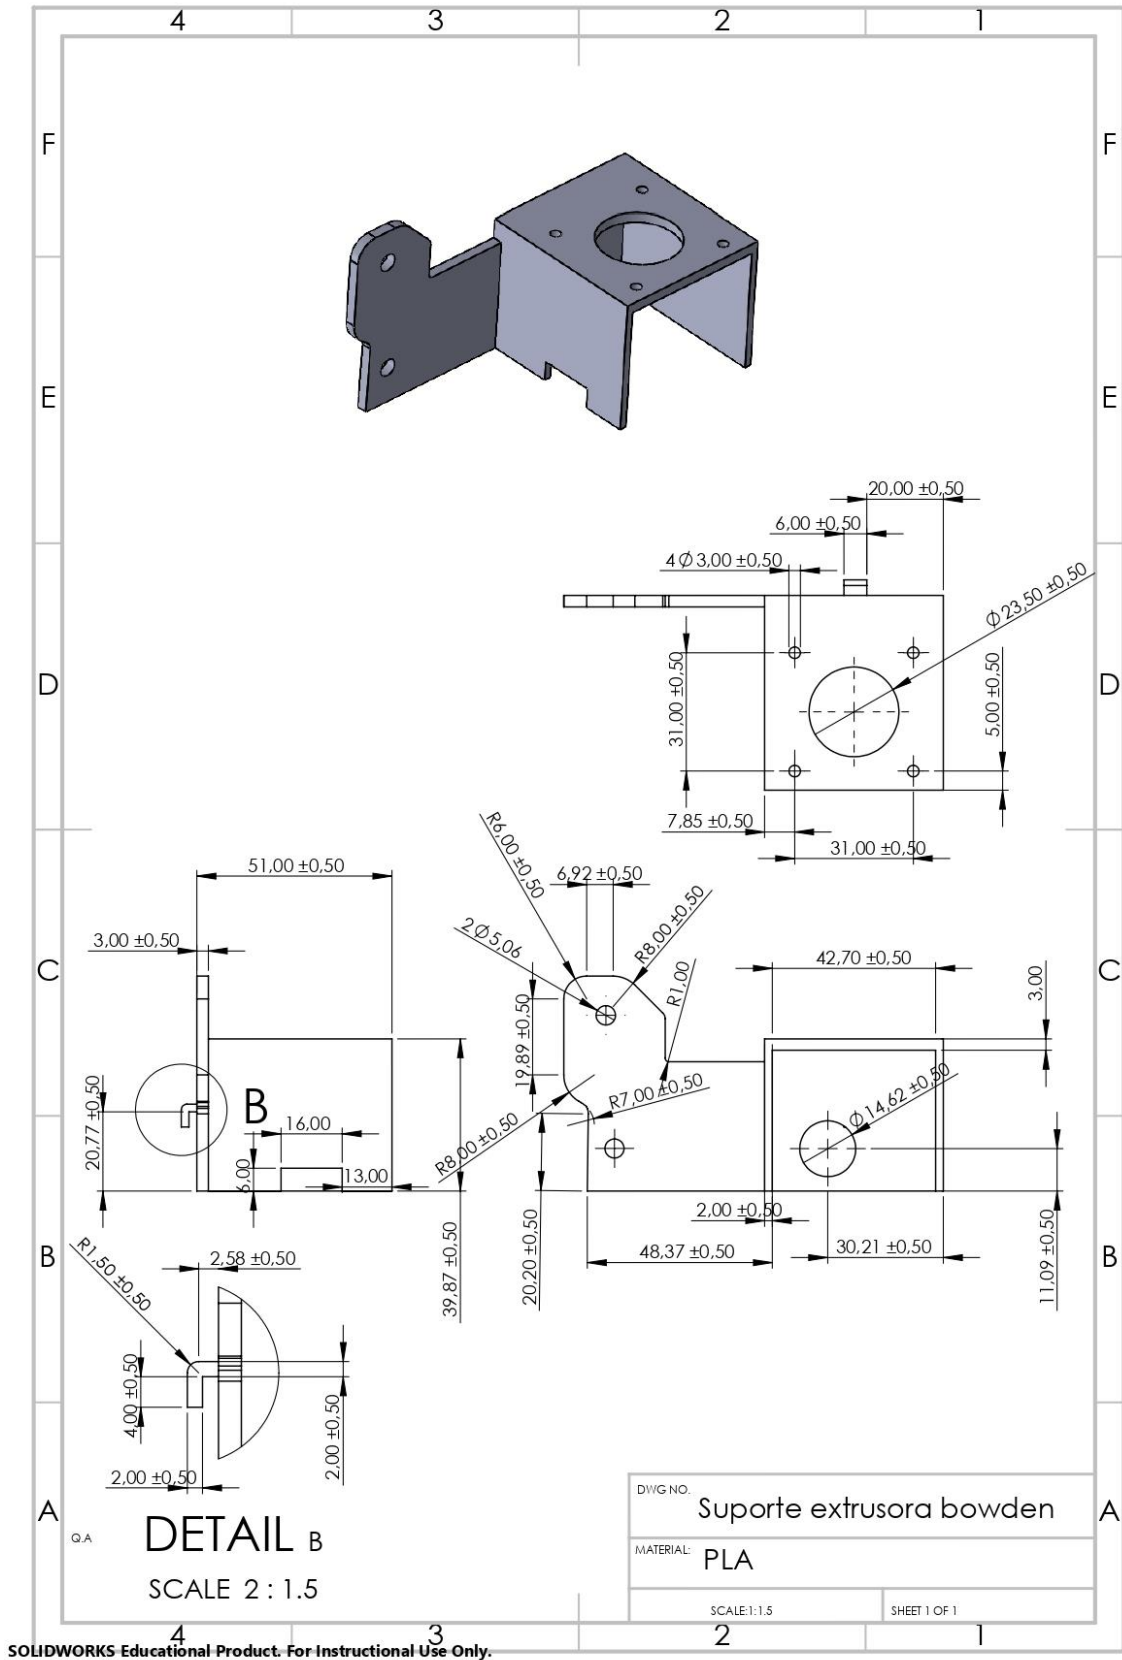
Desenho técnico do suporte da extrusora *bowden*.
